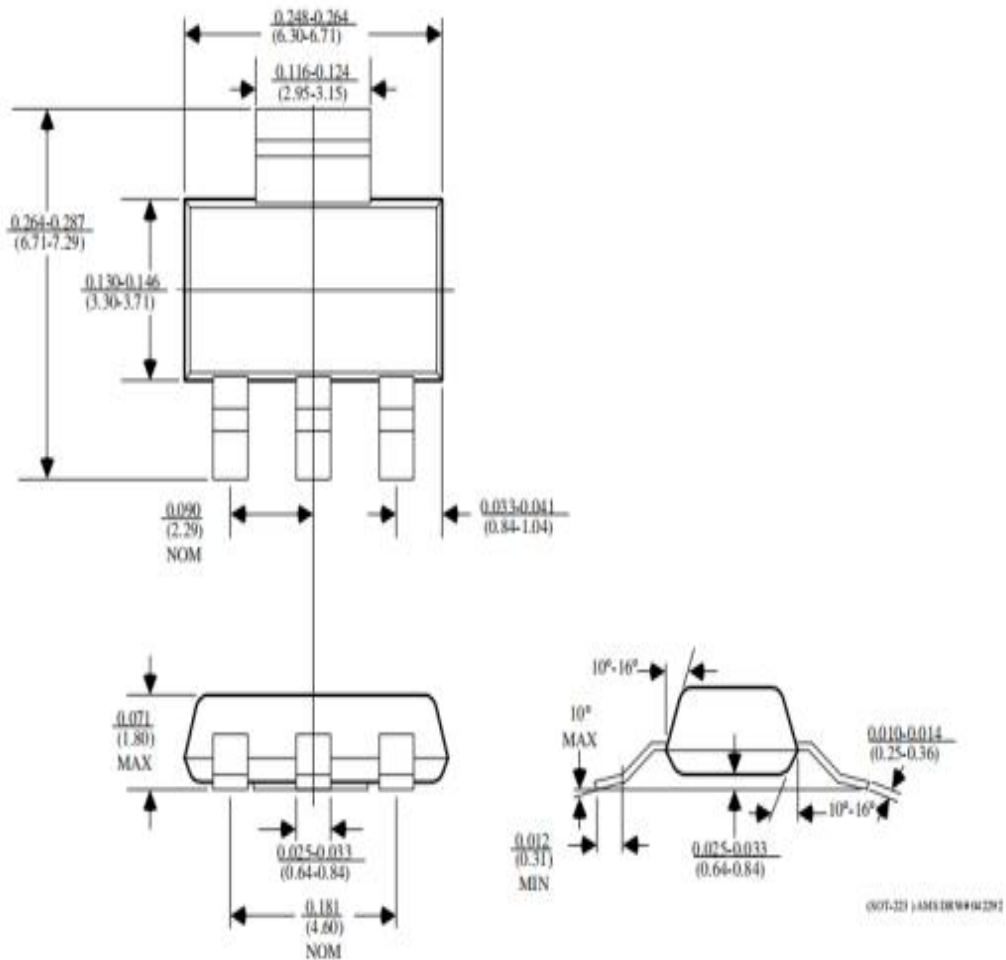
Габаритні розміри стабілізатора LM1117IMPX-3.3/NOPB
